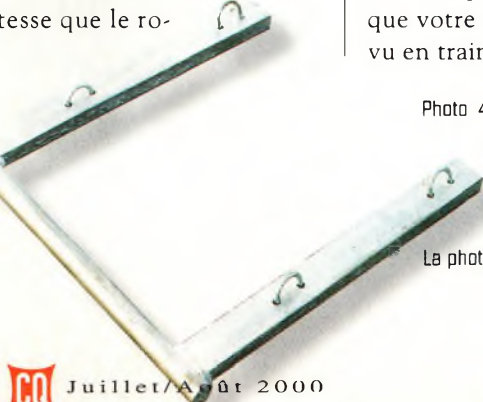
L'adaptateur qui permet l'utilisation d'un support pour maintenir les deux sections d'un pylône pendant les travaux. La photo 5 montre cette pièce en cours d'usage lors des travaux d'installation.
